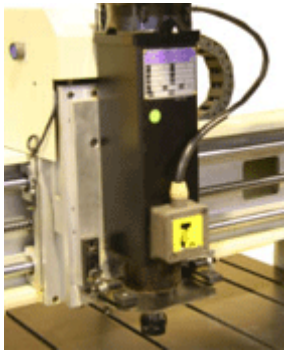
Вертикально-фрезерний верстат з ЧПУ Beaver 9A2
